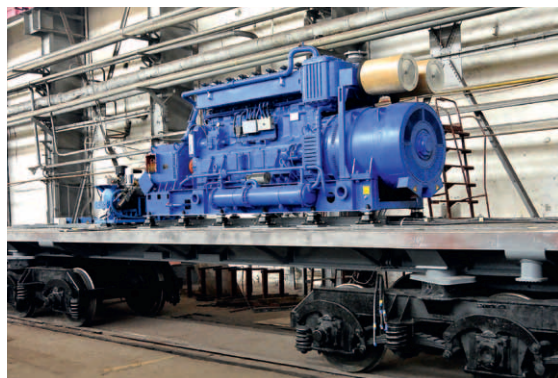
Двигатель, установленный на раме тепловоза. Процесс сборки
